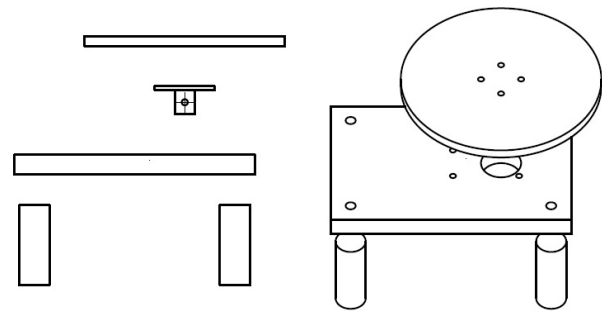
Explosionszeichnung der CAD-Konstruktion des Versuchsstands
